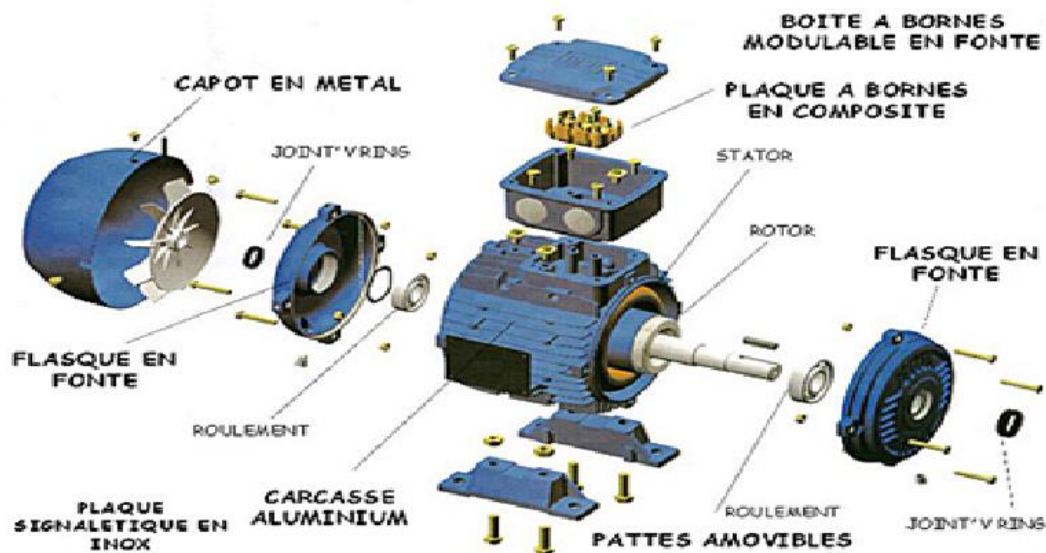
Constitution de la machine asynchrone à cage d'écureuil
